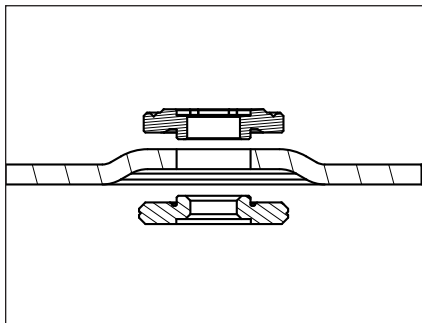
Lato di montaggio del dado di bloccaggio per dischi di spessore grosso
